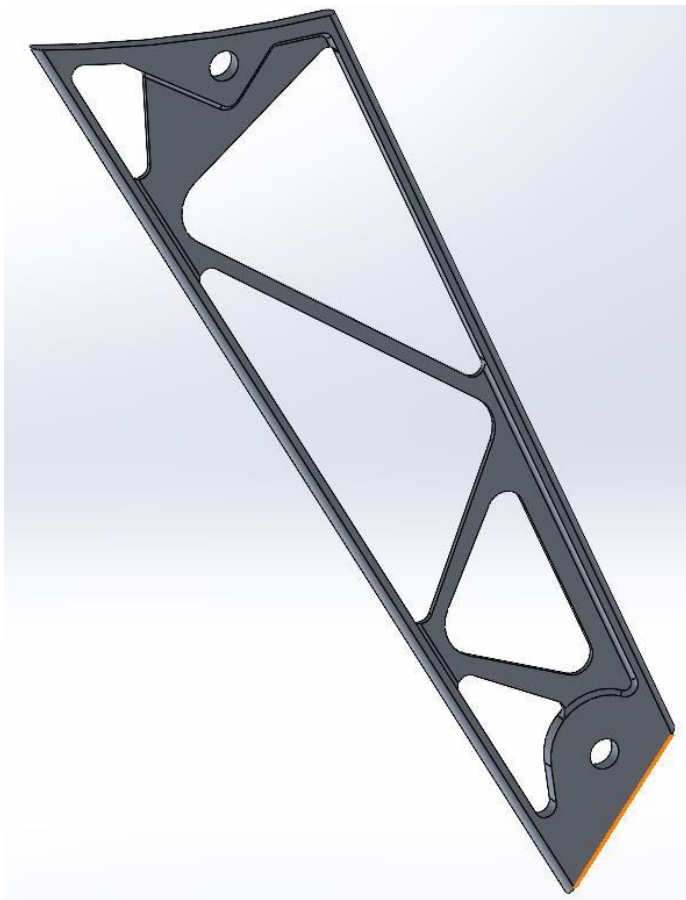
Diseño optimizado para impresión 3D del soporte inferior.
